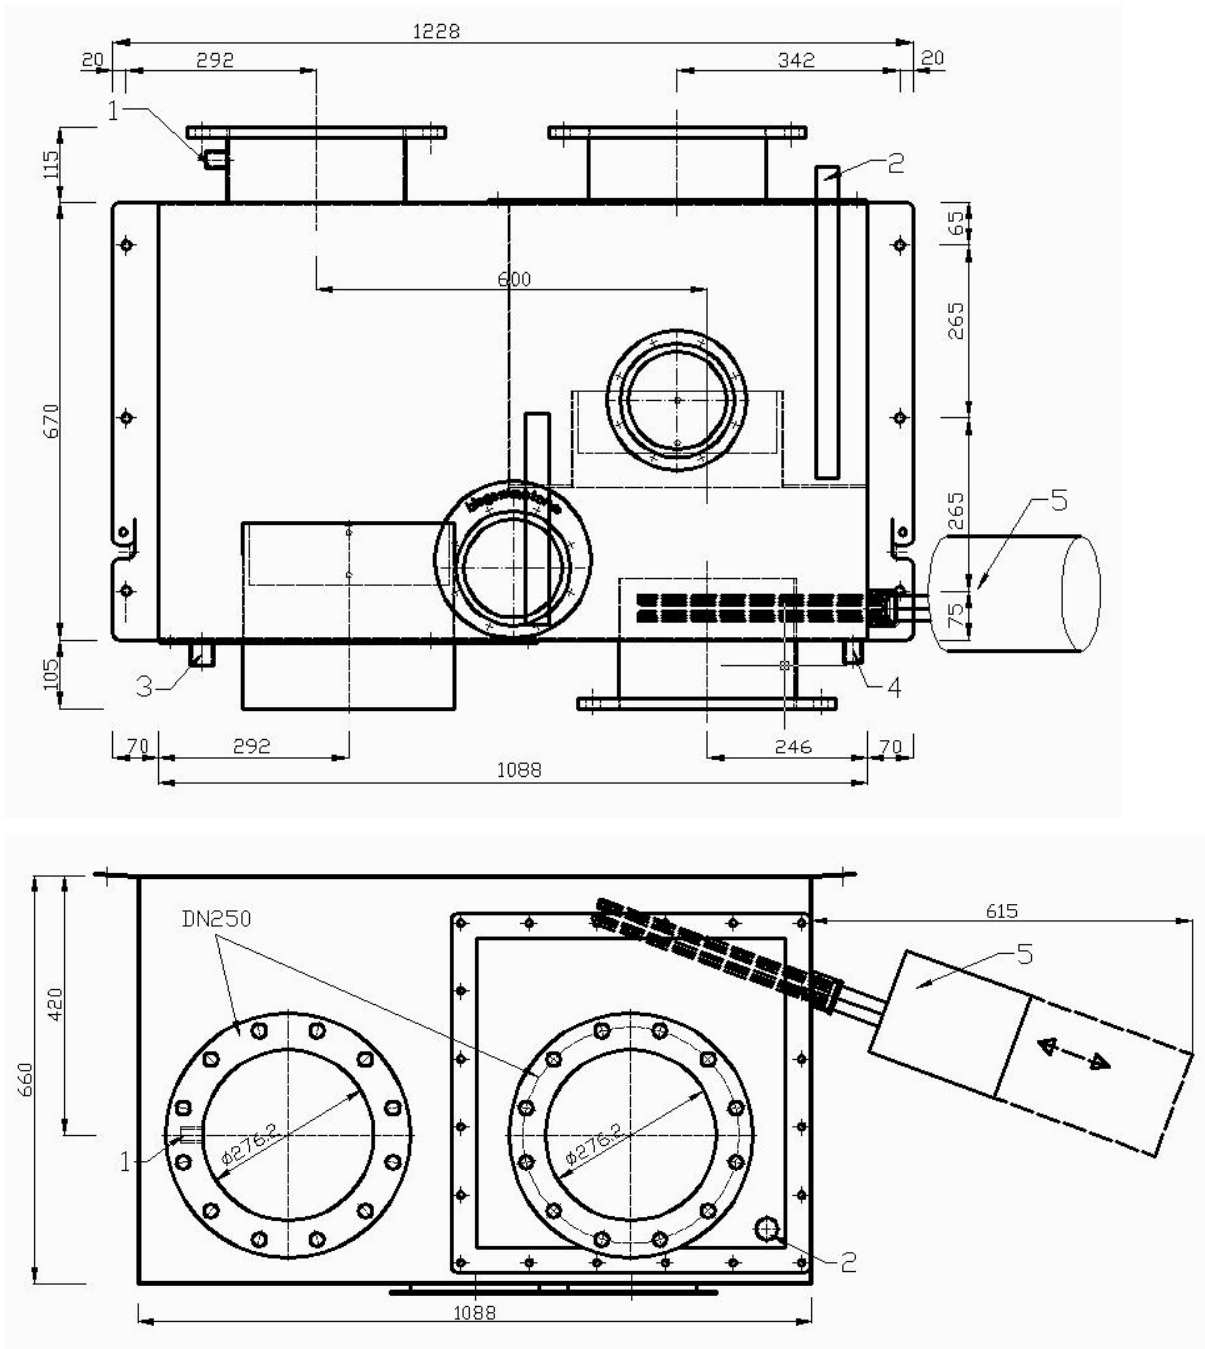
dimensions du régulateur de pression ÜU-TTX 273 (5...10 mbar)
